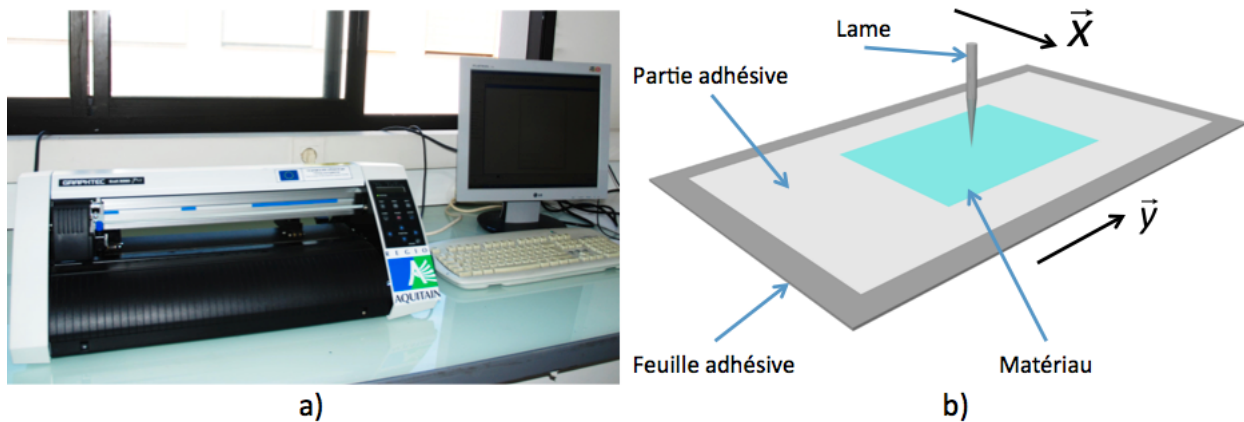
a) Photo de l'imprimante à découpe Craft RoboPro CE6000 (Graphtec), b) Principe de la feuille adhésive sur laquelle on fixe le matériau à découper et axes de déplacement de la feuille et de la lame.
